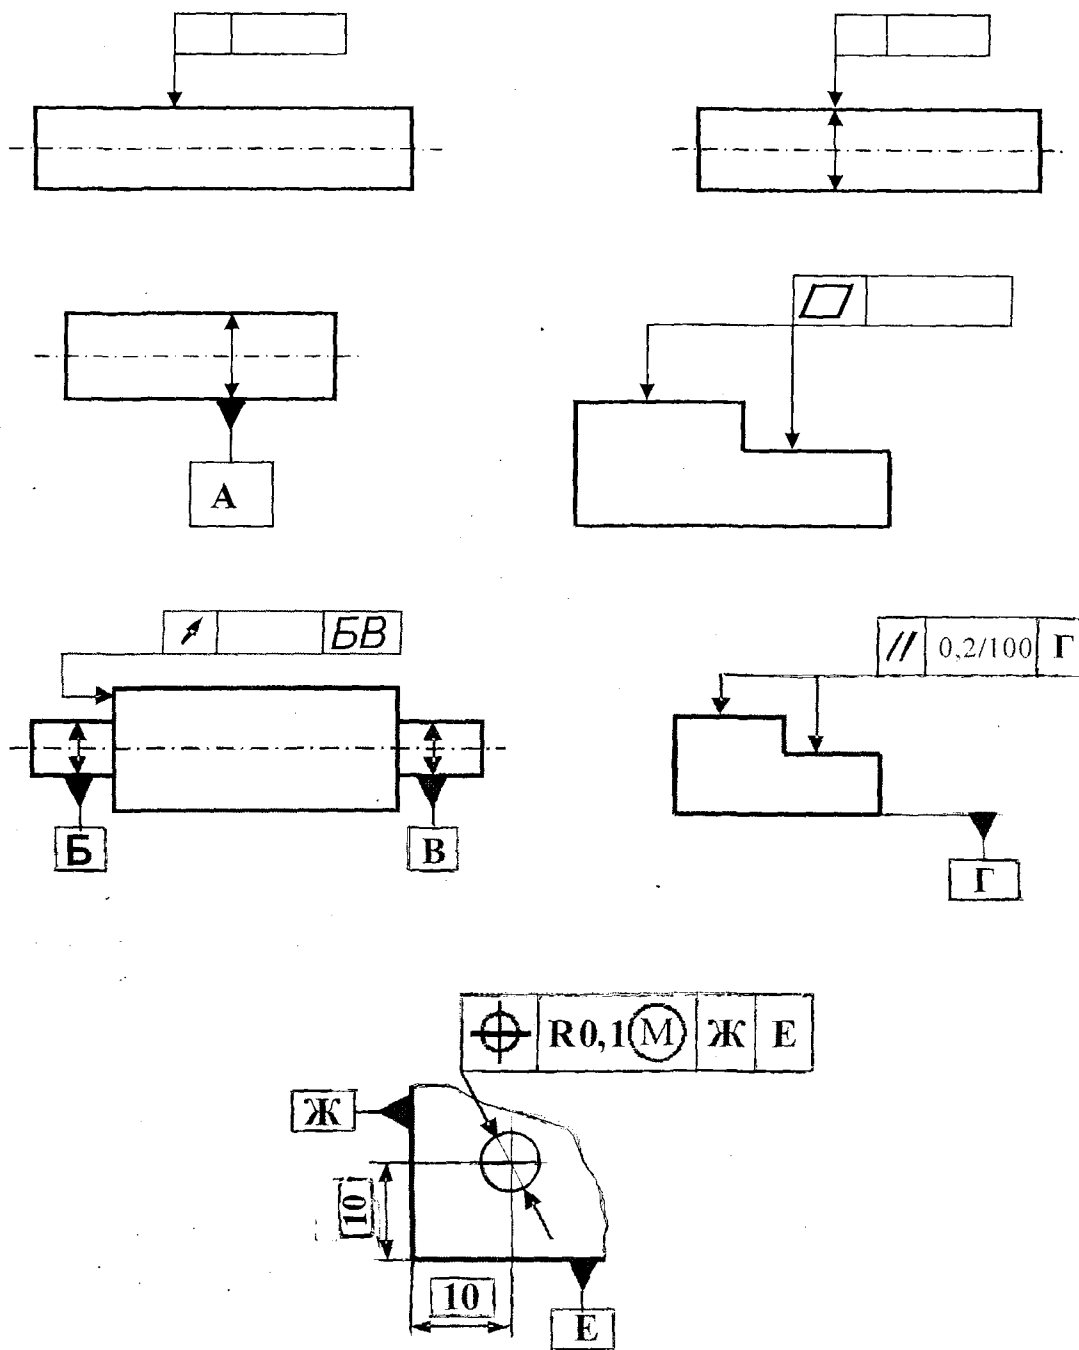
Примеры обозначений допусков формы и расположения поверхностей
